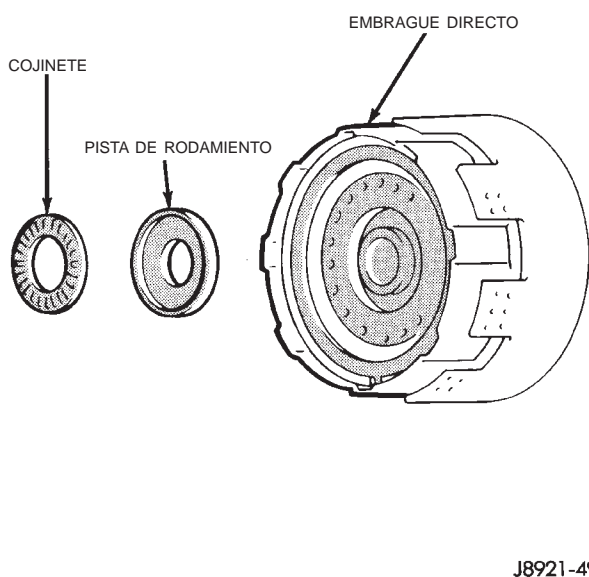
Desmontaje del cojinete y pista de rodamiento de la maza de embrague
